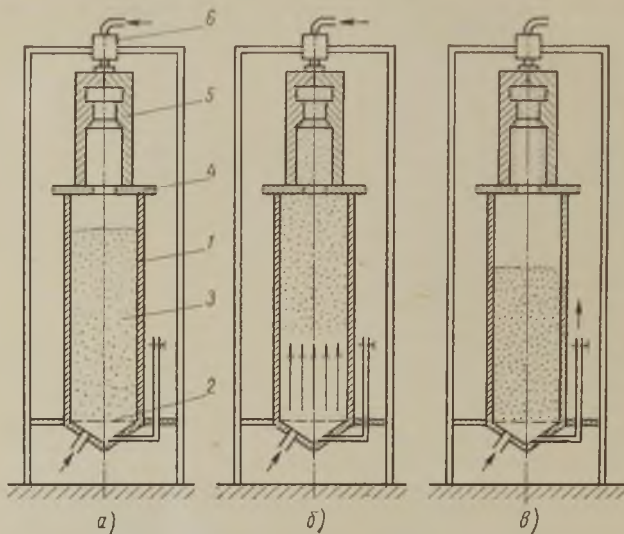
Схема действия установки для изготовления оболочковых стержней
